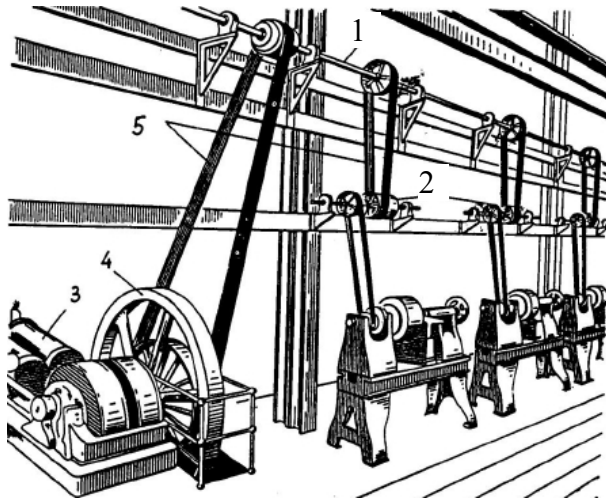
Схема роботи групового привода: 1 – вал; 2 – контрприводи; 3 – парова машина; 4 – маховик; 5 – паси
